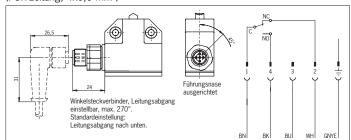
Maßzeichnung/Anschlussplan N01.550/562SVM5 mit Steckverbinder M12 (SVM5, 5-polig)
